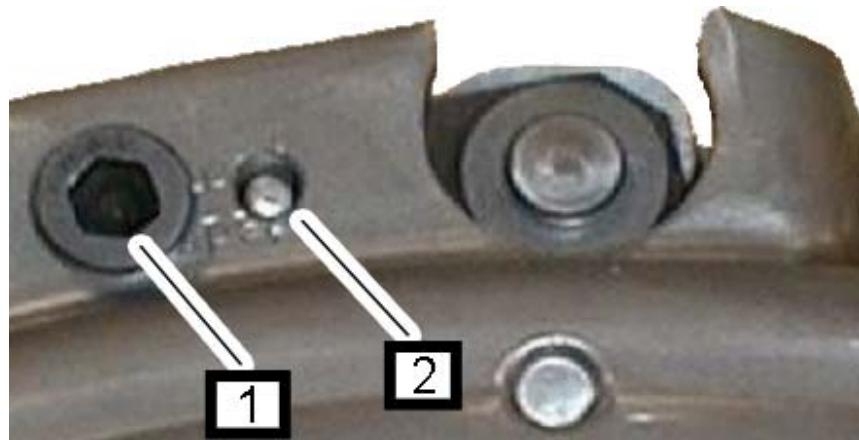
1 Anschlagschraube / Stop Screw / Vis de blocage / Tornillo de bloqueo
